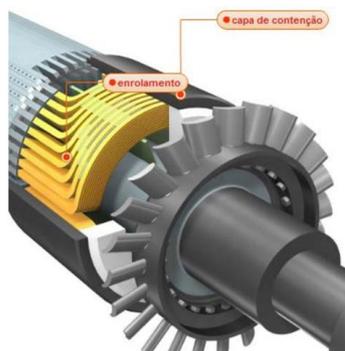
Desenho demonstrativo do enrolamento das bobinas do rotor, com os terminais sob a capa de contenção.
